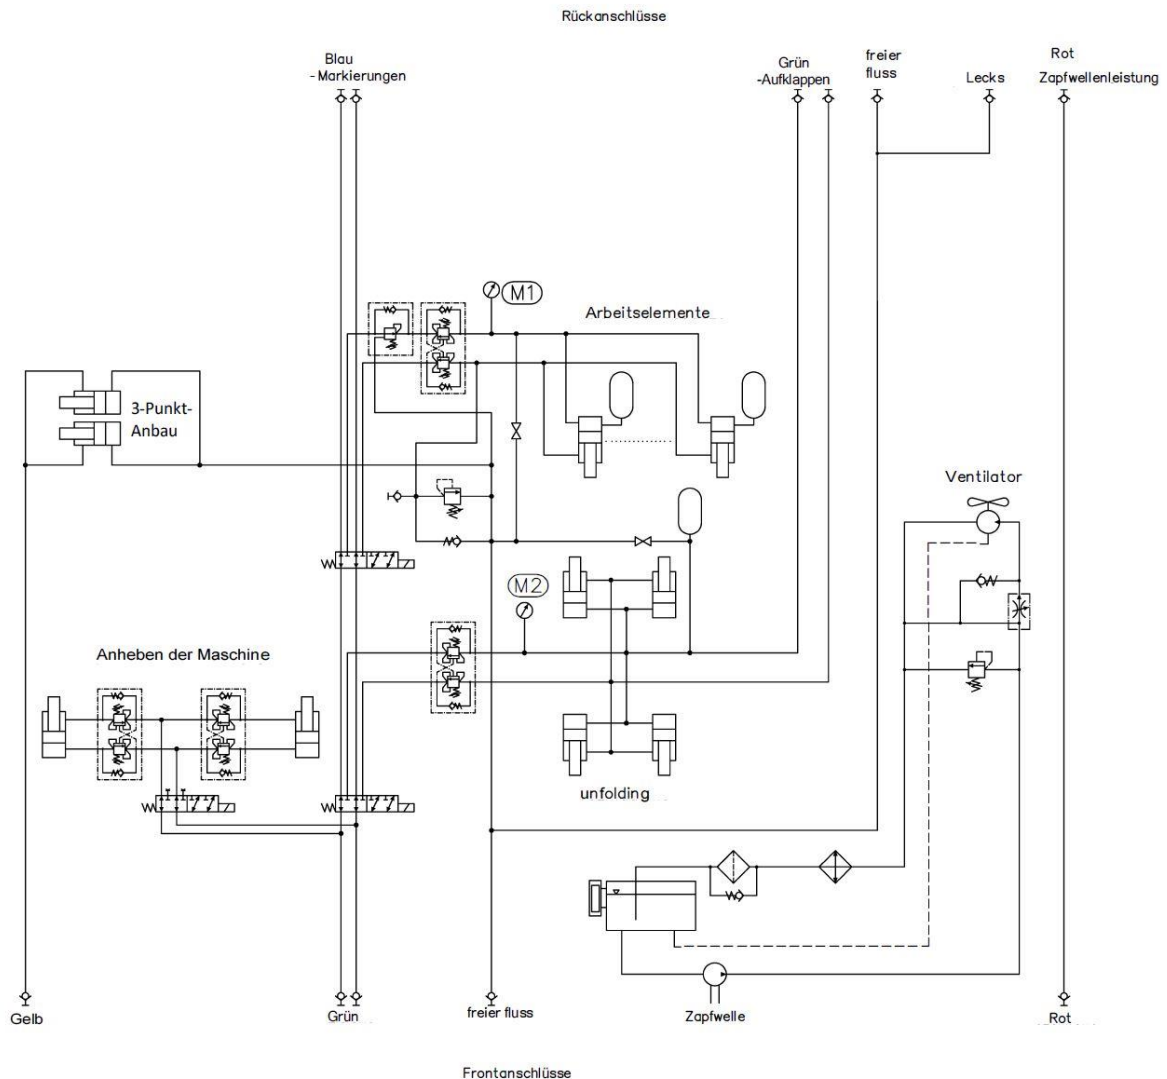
Plan der Hydraulikanlage STK 400 mit externer Hydraulikanlage.
